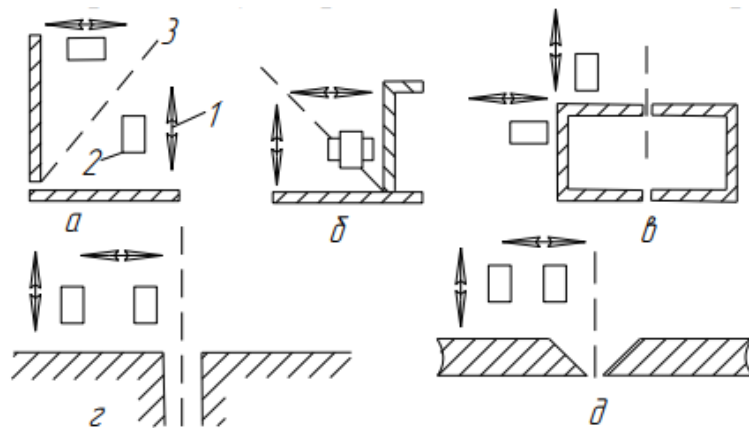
Типи та конструкції зварних з'єднань: а – кутове (зсередини); б – таврове, з однією вузькою полицею; в – стикове (при точних розмірах елементів, що зварюються,); г – стикове, у вузький глибокий зазор; д – стикове, з обробленням кромки; 1 – напрямок переміщення; 2 – датчик; 3 – вісь зварювального електрода
